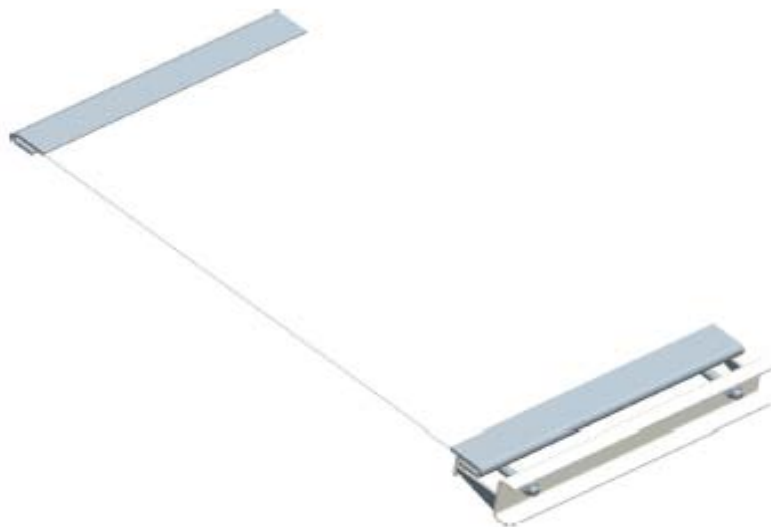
Ensamble tela metálica reforzada con tensor (sistema tamiz)
